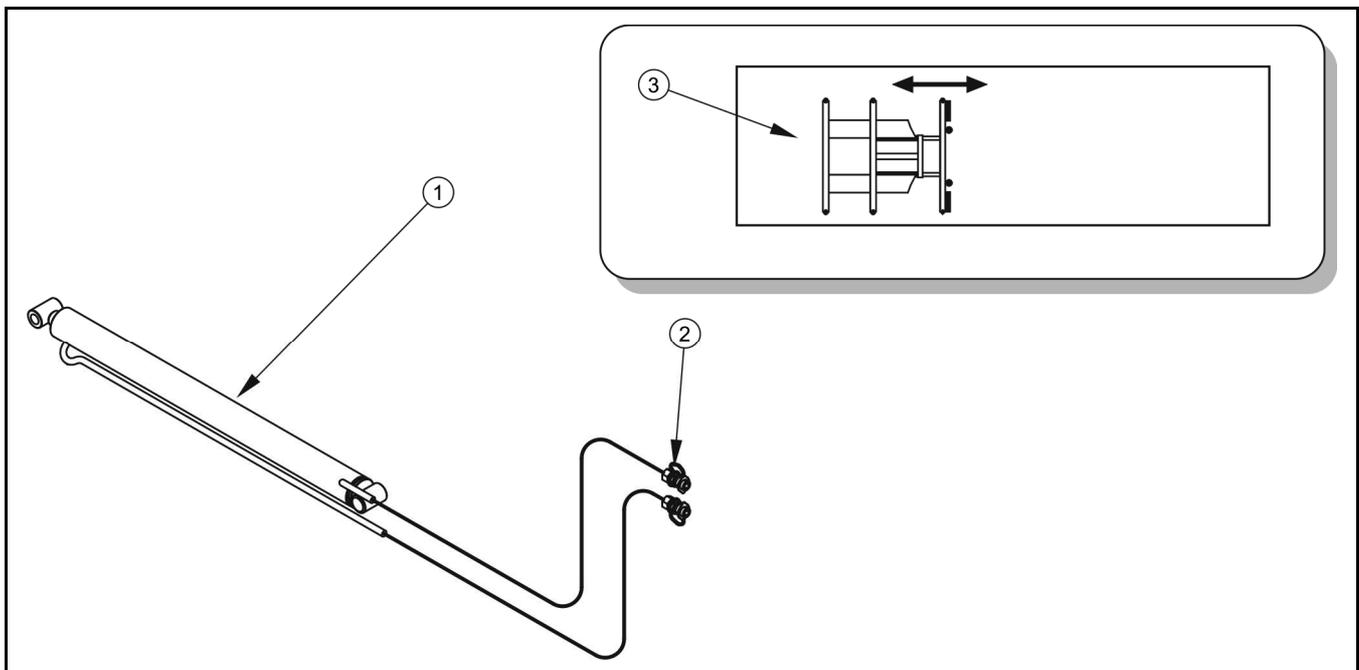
A Installation hydraulique d'allongement du chassis.
